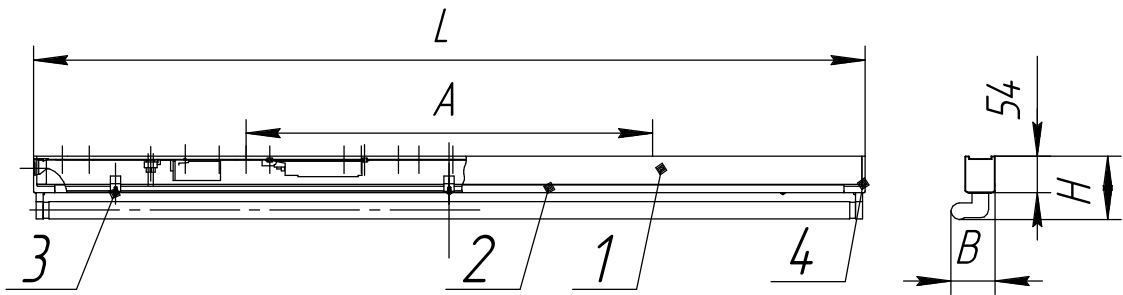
1. Корпус в сборе, 2. Крышка, 3. Винт, 4. Крышка.
